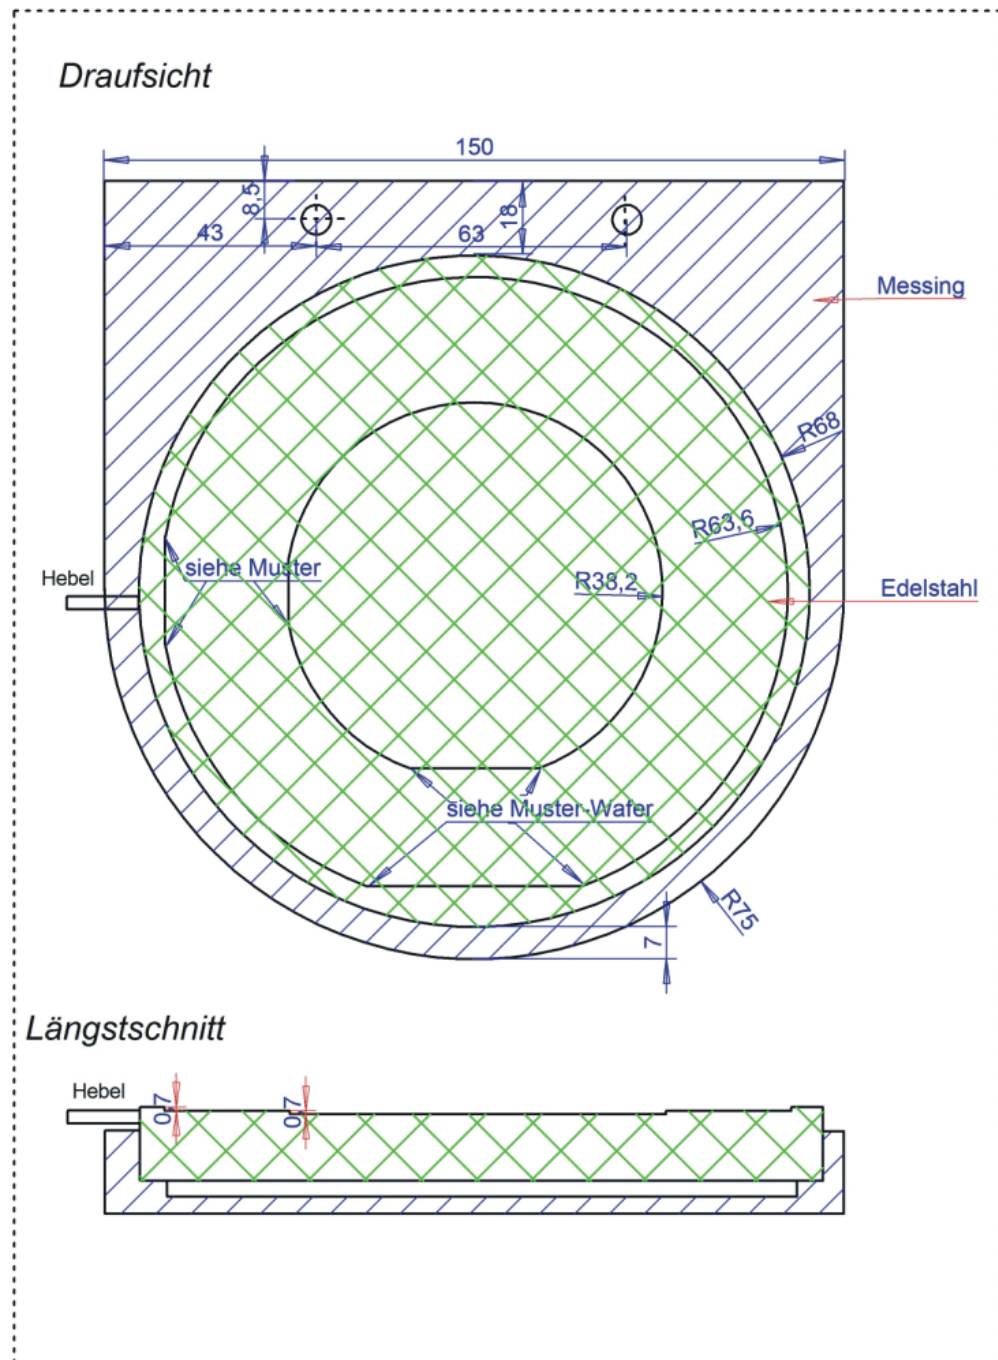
Technische Zeichnung des Drehtellers. Alle Angaben in mm
